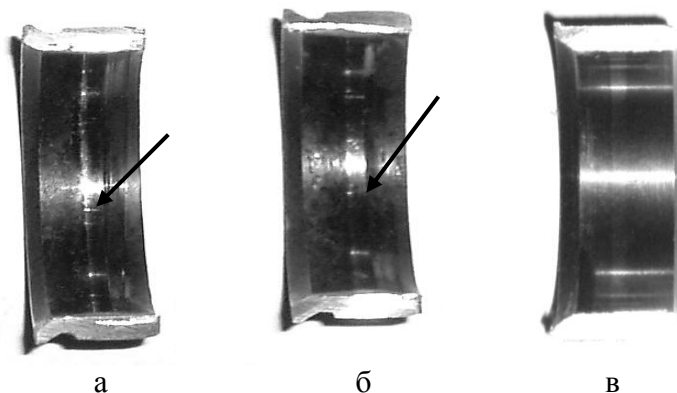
Следы износа втулки корпуса среднего турбокомпрессора ТКР-11Н-1 после эксплуатационных испытаний: а – ремонтная втулка установленная в корпус турбокомпрессора по стандартной технологии после 1736 мото-часов; б – втулка нового турбокомпрессора после 1814 мото-часов; в – втулка установленная в корпус турбокомпрессора с натягом объемным электромеханическим дорнованием после 1782 мото-часов
